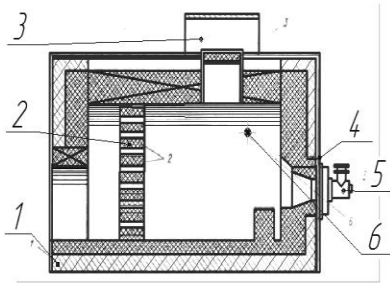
Камерна установка для спалювання стічних вод: 1 – футеровка; 2 – газорозподільні ґрати; 3 – підривний клапан; 4 – кожух; 5 – пальник; 6 – форсунка для розпилювання стоків
